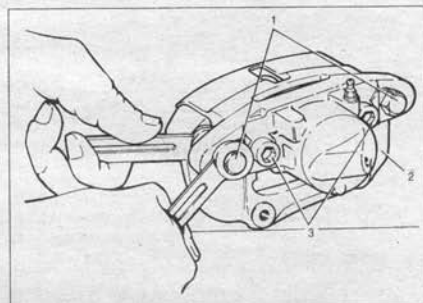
Отвертывание болта крепления цилиндра: 1 – болты крепления цилиндра; 2 – цилиндр; 3 – болты, стягивающие цилиндр с суппортом
